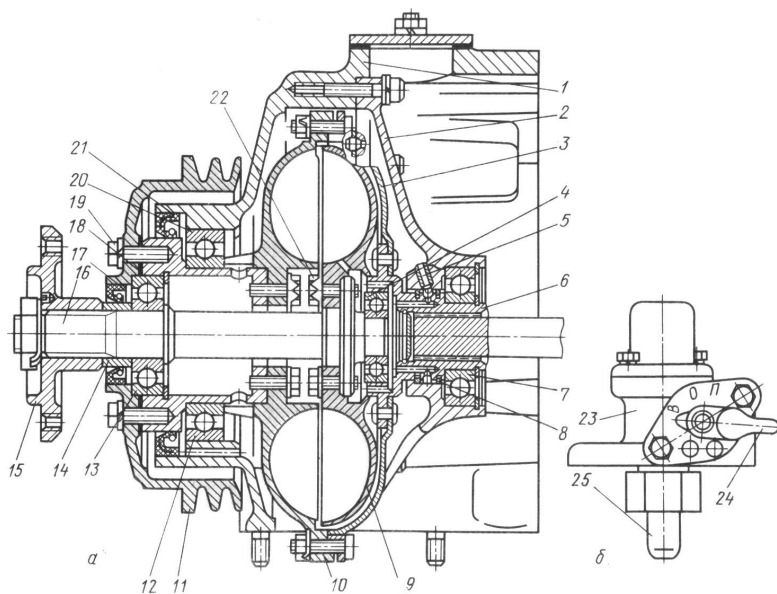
Гидромуфта привода вентилятора: а – конструкция; б – включатель гидромуфты: 1 – передняя крышка; 2 – корпус; 3 – кожух; 4, 7, 12, 13 и 20 – шарикоподшипники; 5 – трубка подвода масла; 6 – ведущий вал; 8 – уплотнительное кольцо; 9 – ведомое колесо; 10 – ведущее колесо; 11 – шкив; 14 – упорная втулка; 15 – ступица вентилятора; 16 – ведомый вал; 17 и 21 – самоподжимные сальники; 18 – прокладка; 19 и 22 – болты; 23 – корпус включателя; 24 – рычаг пробки крана; 25 – термосилового датчик.
